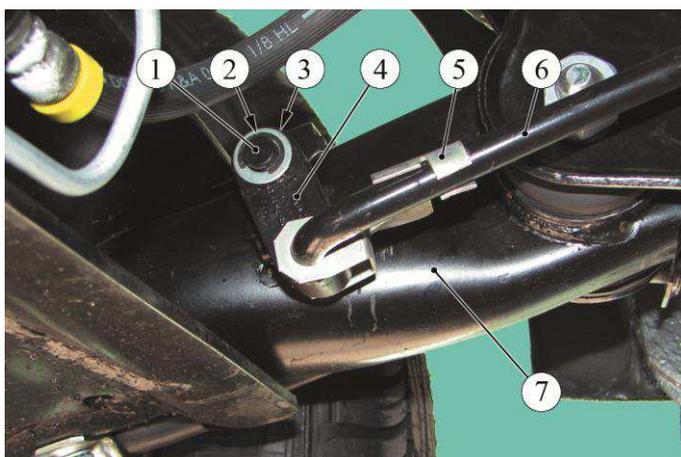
Элементы крепления рычага привода регулятора давления:
